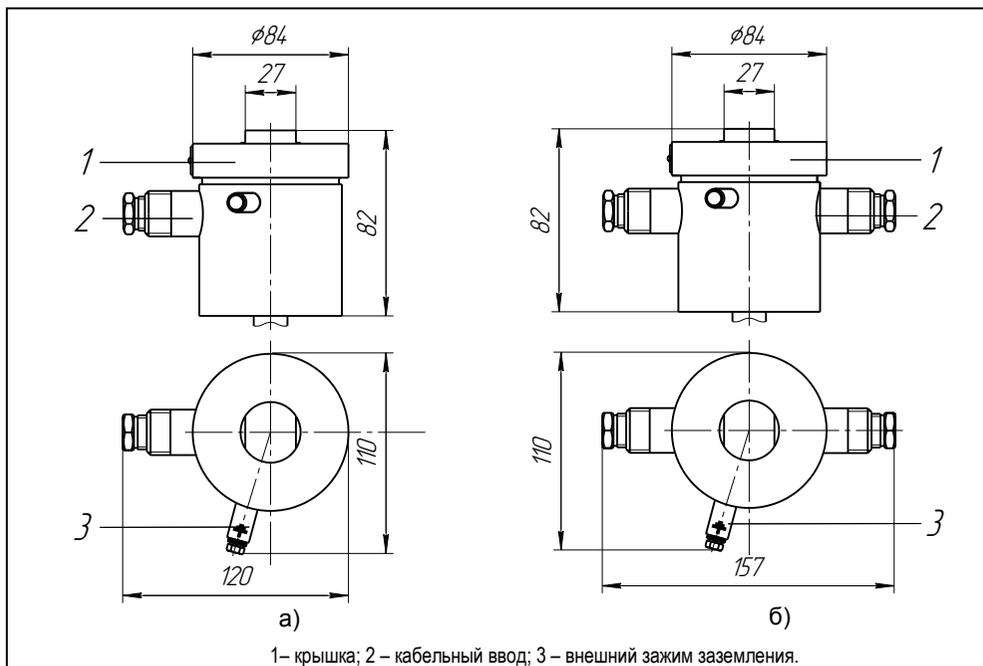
Варианты исполнения корпуса ПМП-185:
